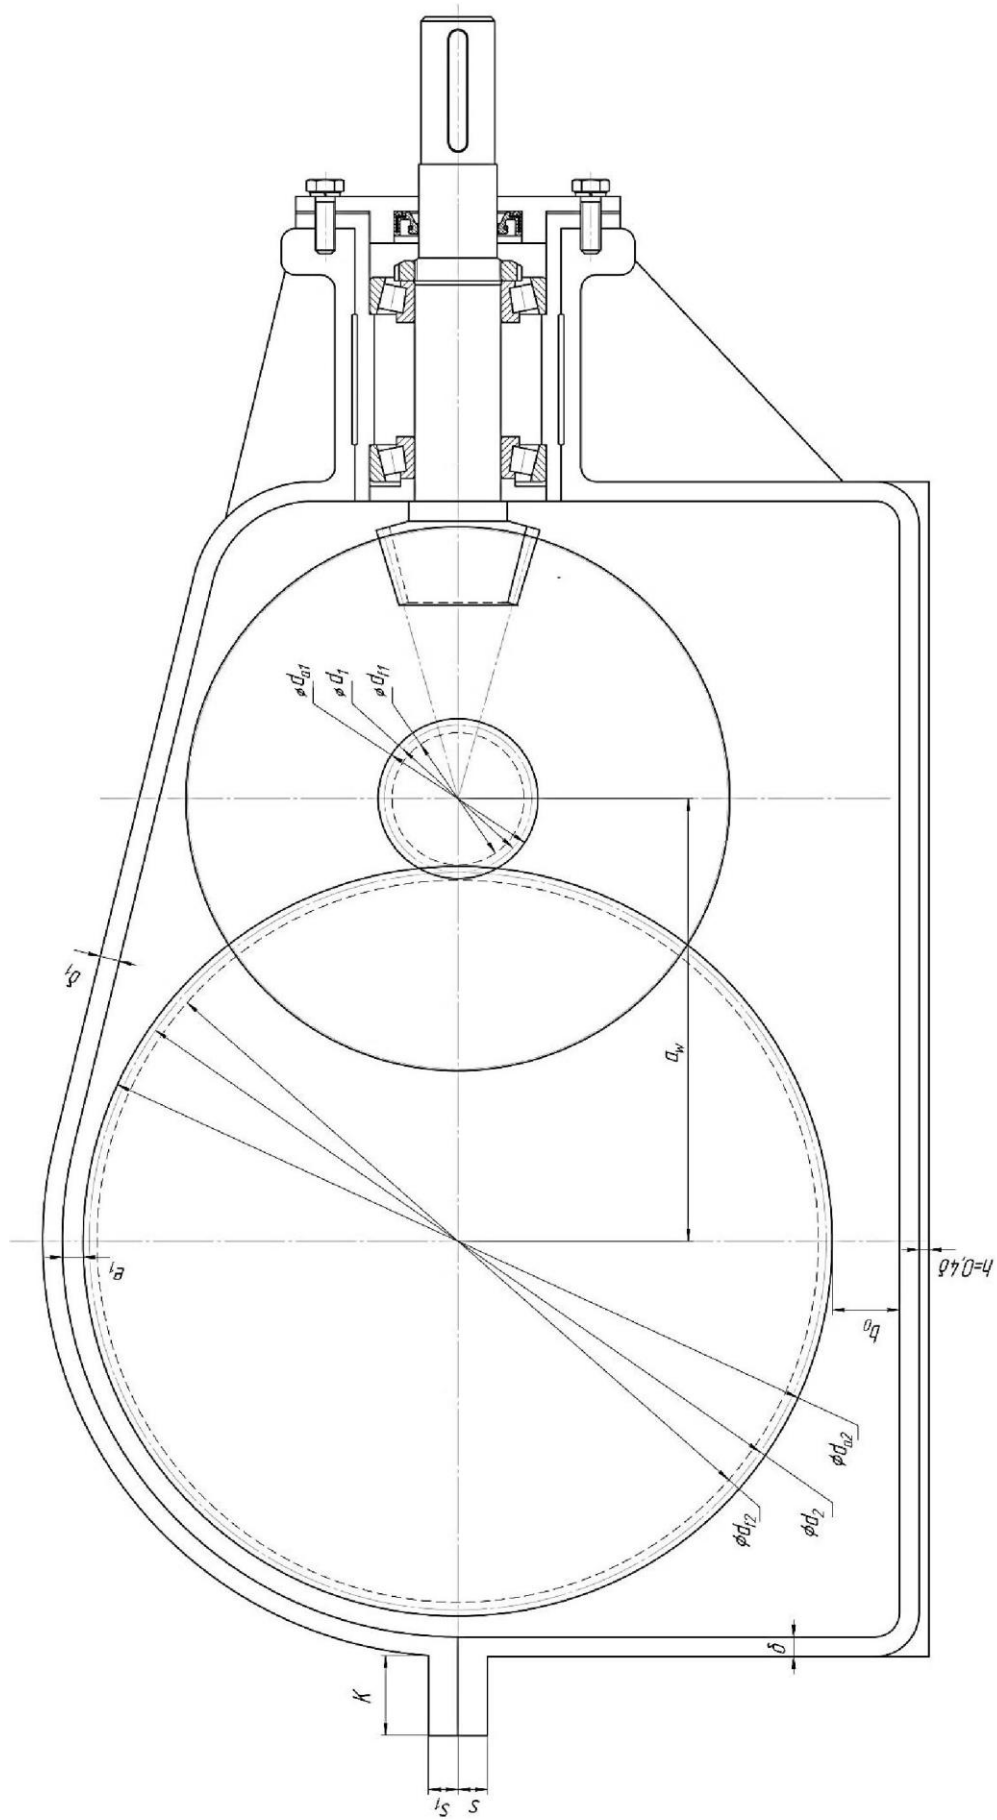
Компонувальне креслення конічно-циліндричного редуктора (початок)
